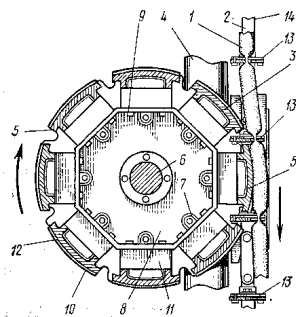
Приспособление для удаления колбасных батонов из формовочного устройства.
